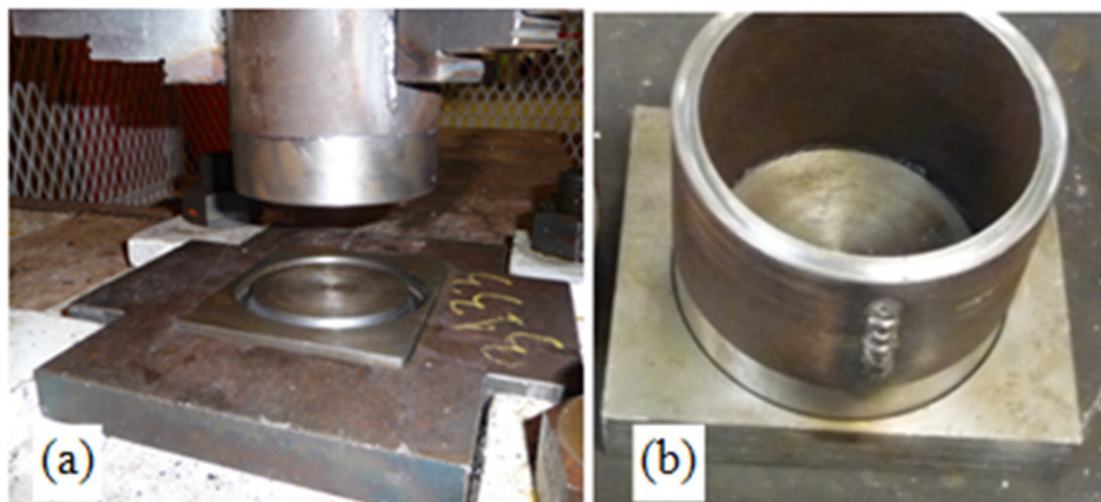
Fixação na máquina em (a) e tubo soldado com chapa em (b).
